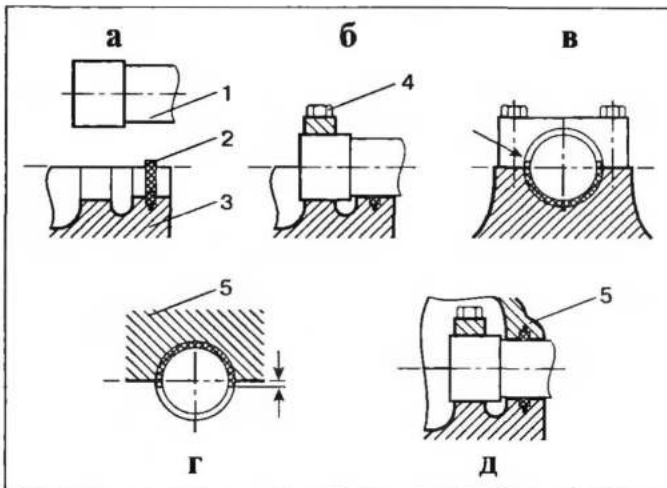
Подготовка уплотнения коленчатого вала с сальниковой набивкой при сборке двигателя:
